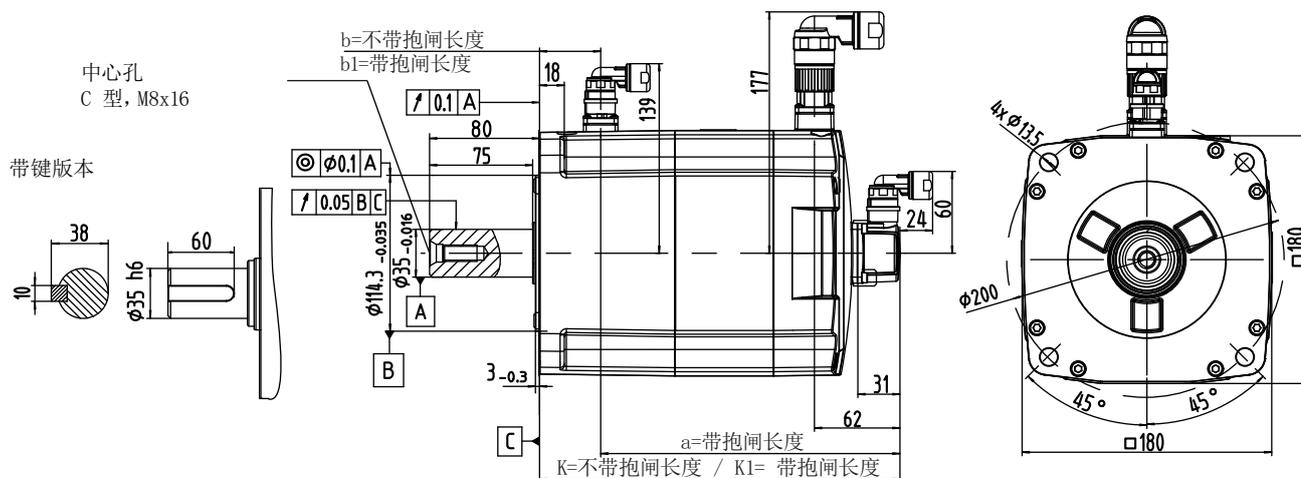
电机安装尺寸 (mm) - 轴高: 90 mm, 带绝对式编码器
